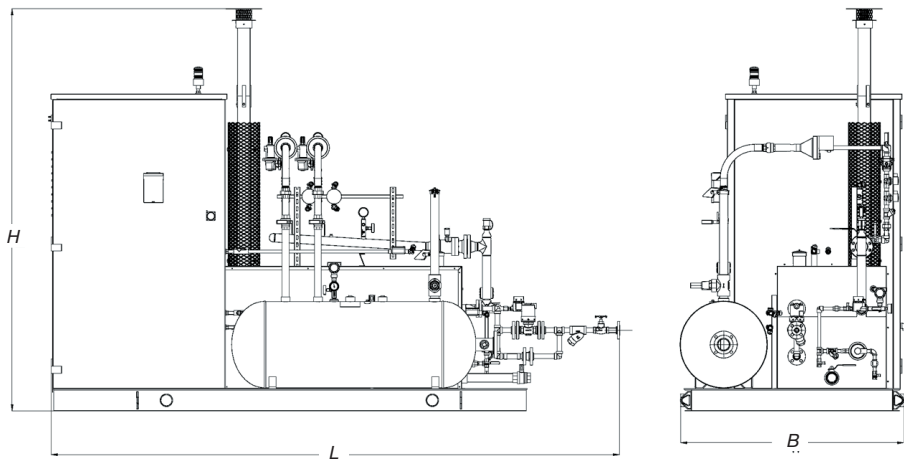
Габаритные размеры установки смесительной Metan-3-2-400(-7000)-B
